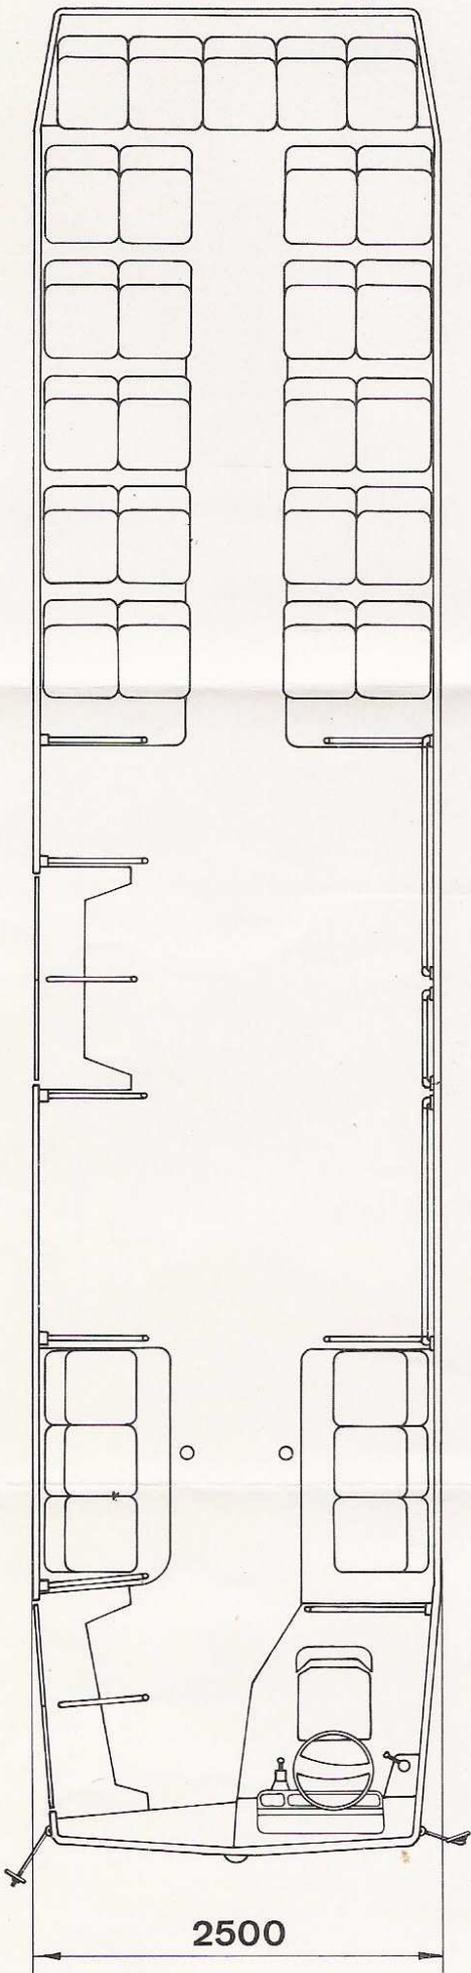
AUTOBUS 6050. Dimensiones principales
